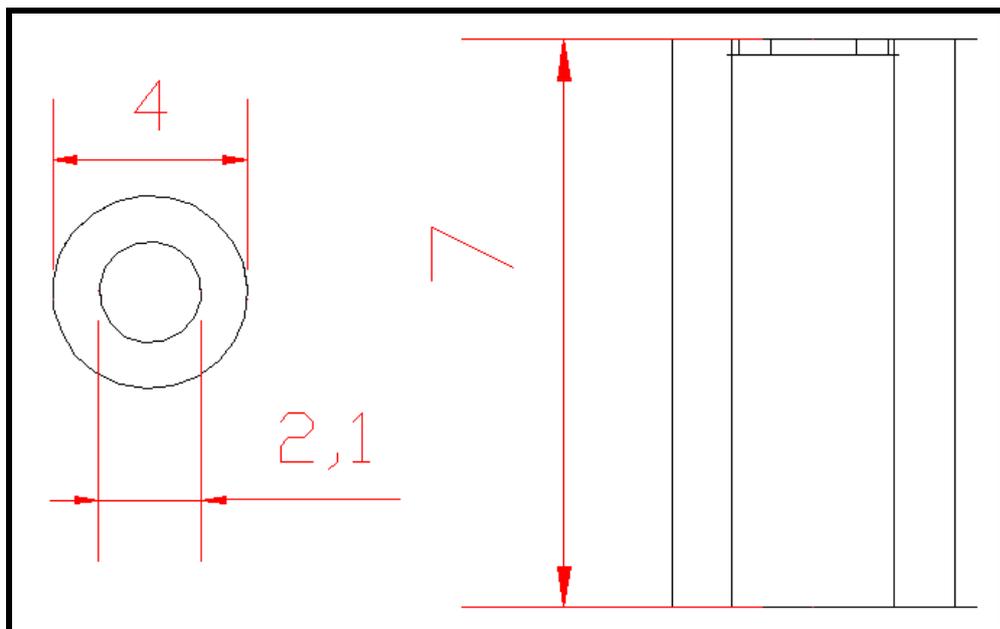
3. Vista Superior y Lateral del Cilindro (Dimensiones en cm.)
